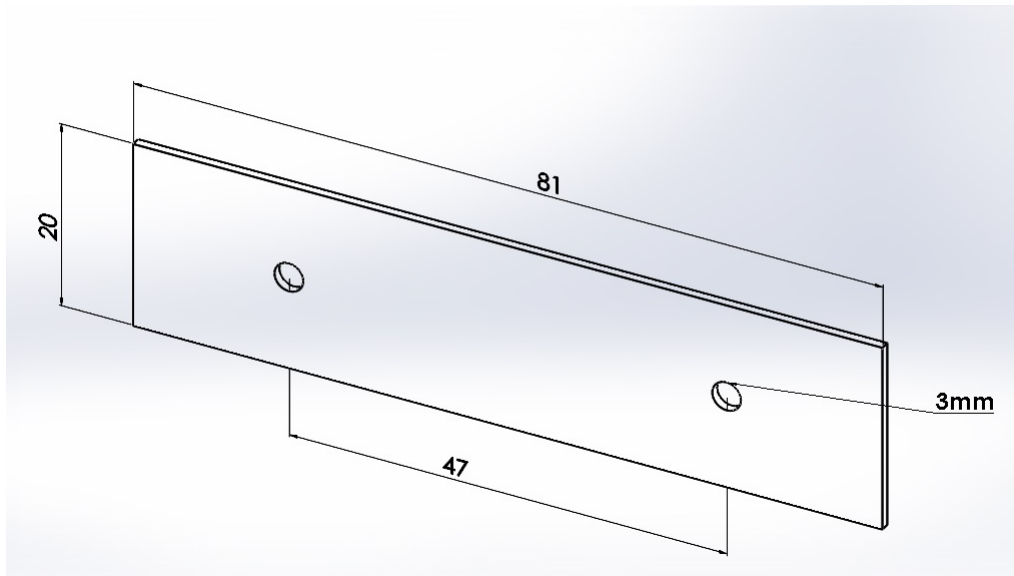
desenho técnico para auxiliar na construção do componente 4: placa fim de curso.
